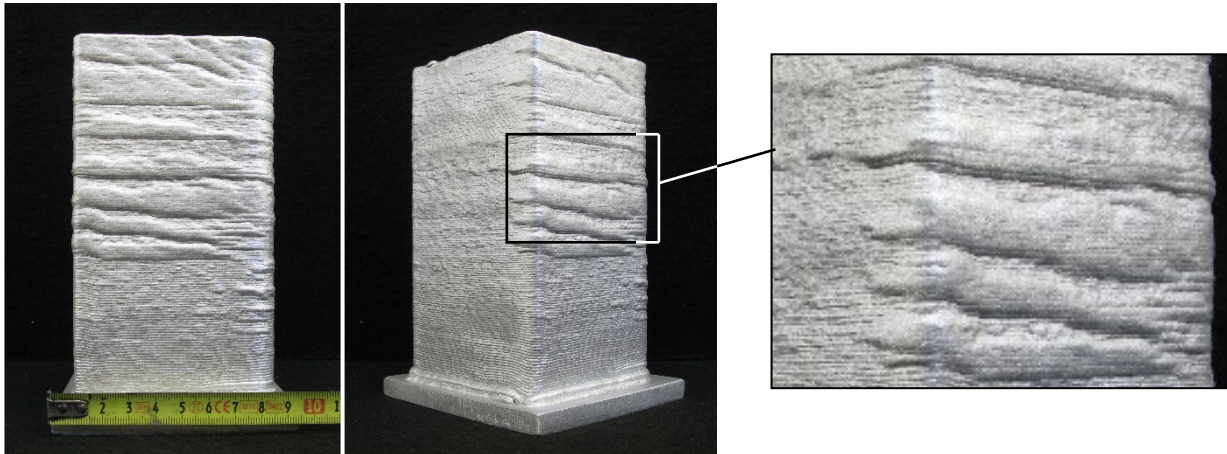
Seiten- und Schrägansicht eines mittels WAM gefertigten Profils mit Rechteckquerschnitt
